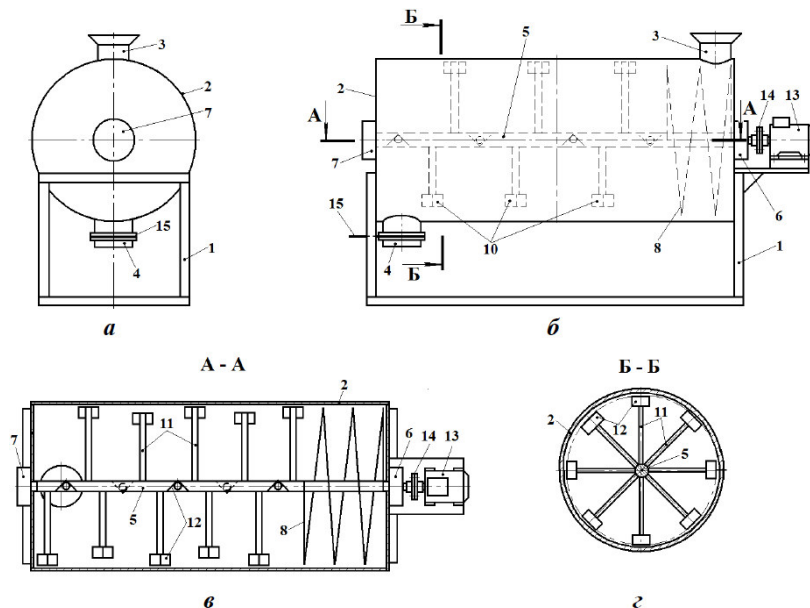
Устройство для приготовления комбикорма: а - общий вид, б – вид сбоку; в - продольный разрез устройства по линии А-А, г – поперечный разрез устройства по линии Б-Б (обозначения в тексте)
